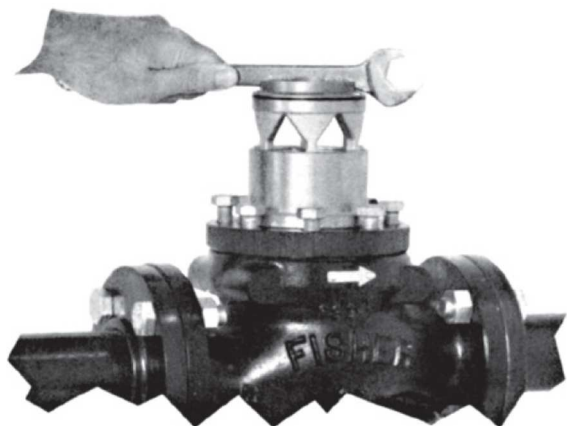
Демонтаж или установка седлового кольца/клетки с использованием корпуса в качестве удерживающего устройства
